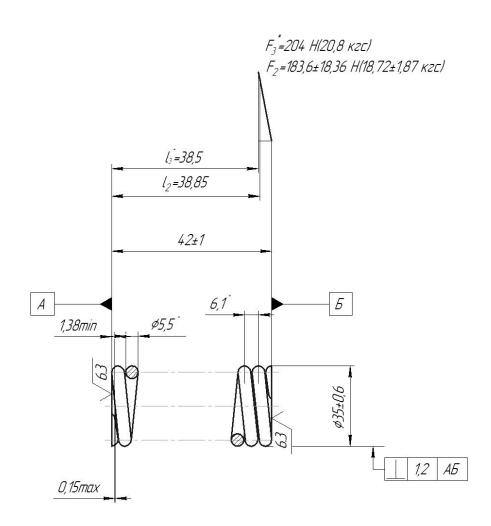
Эскиз пружины сжатия главного цилиндра
